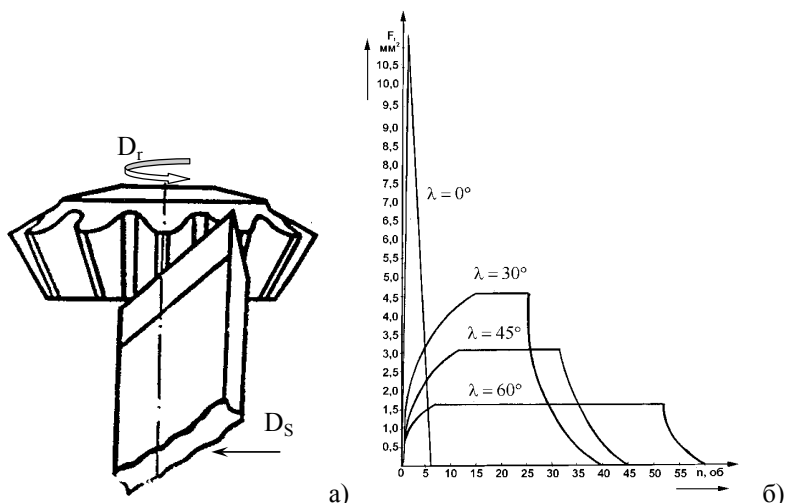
Обработка заготовки с предварительно штампованными зубьями широким резцом с большим углом наклона режущей кромки и тангенциальной подачей
